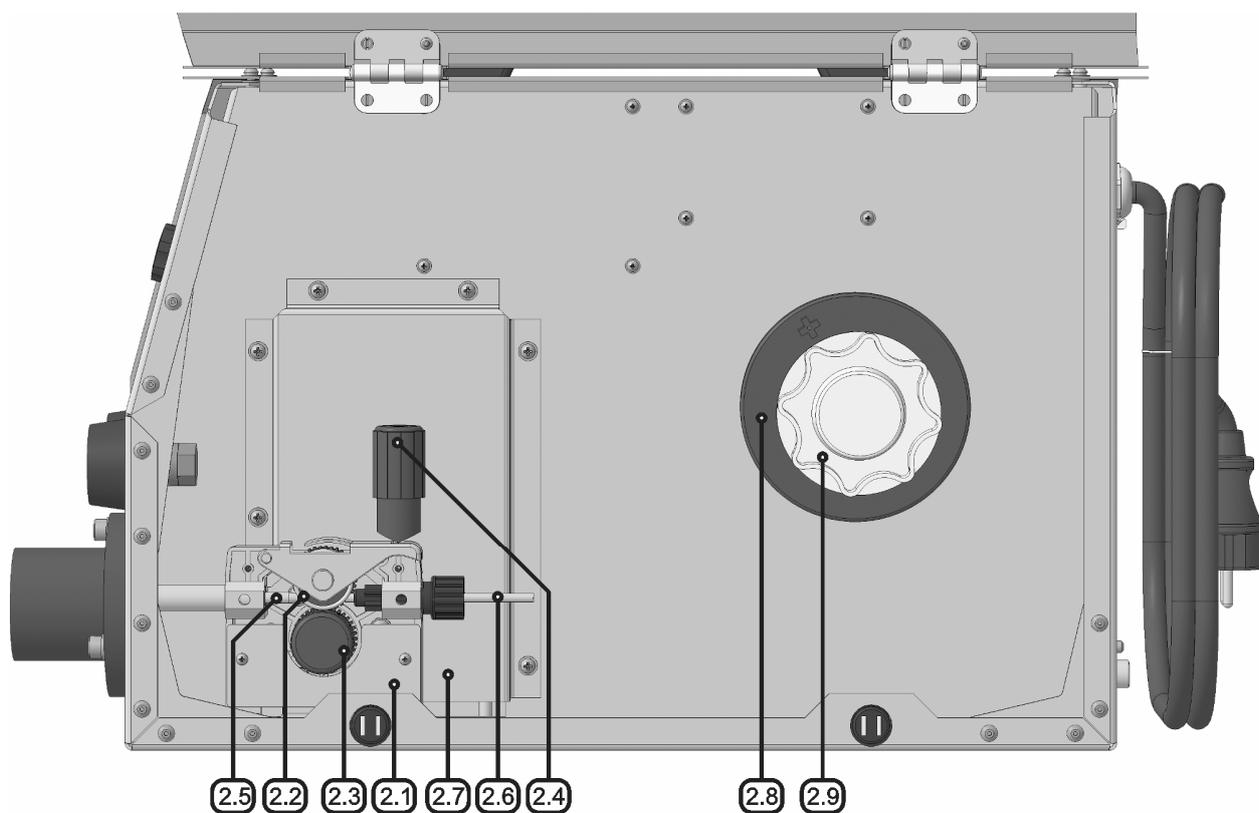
Внешний вид отсека механизма подачи сварочной проволоки
